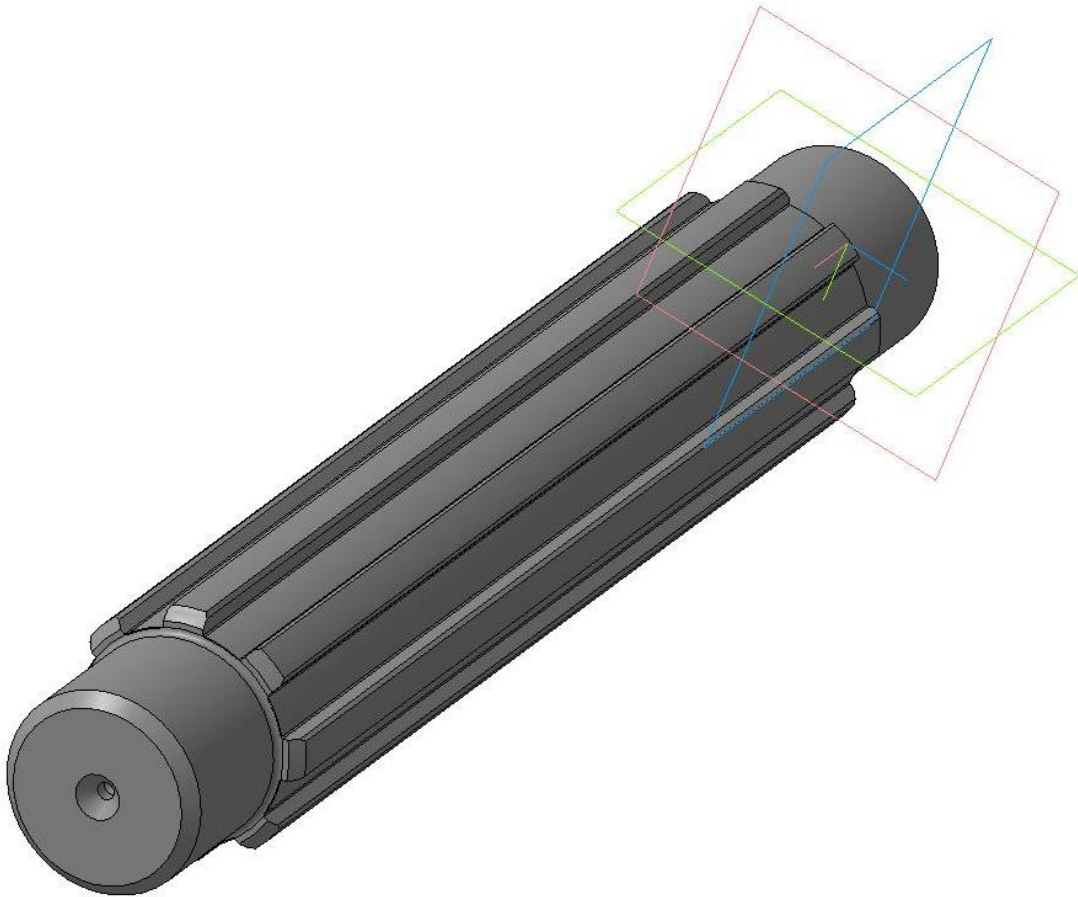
Зовнішній вигляд 3D-моделі деталі «Вал шліцьовий» коробки швидкостей токарно-гвинторізного верстата 1А62
